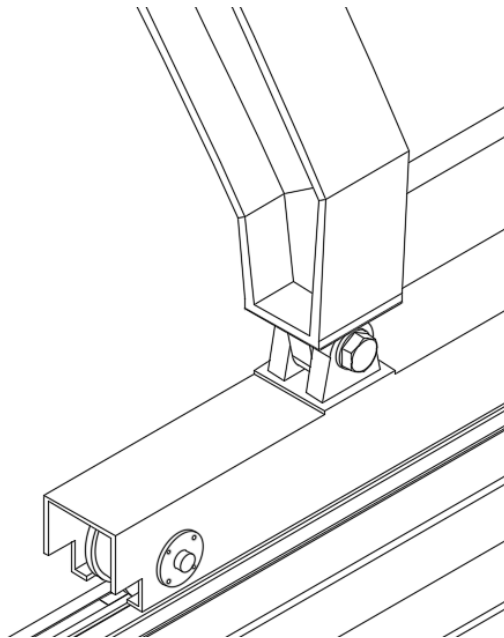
Diseño de Unión Viga Principal con Viga Testera
